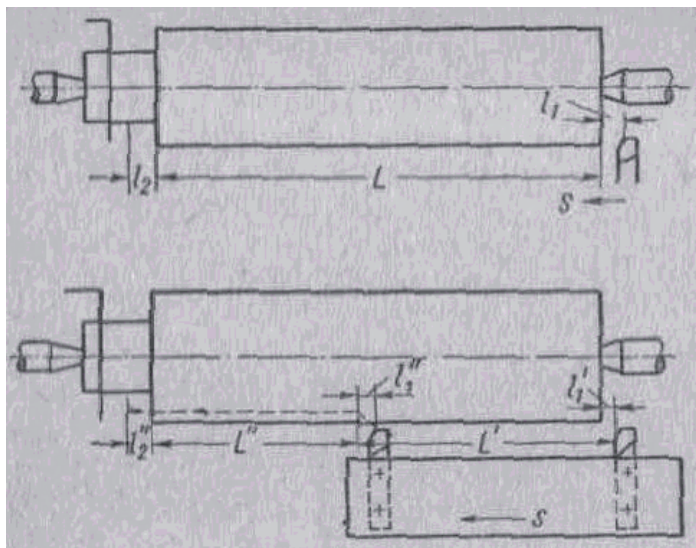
Схема точения одной поверхности вала двумя проходными резцами
